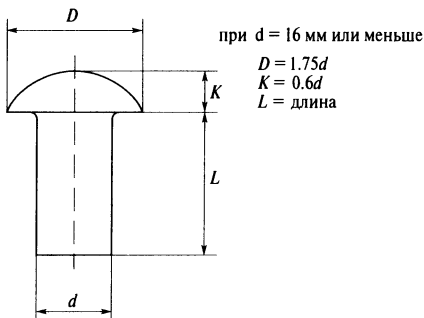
Полукруглая головка заклепки, изготовленная методом холодной штамповки
